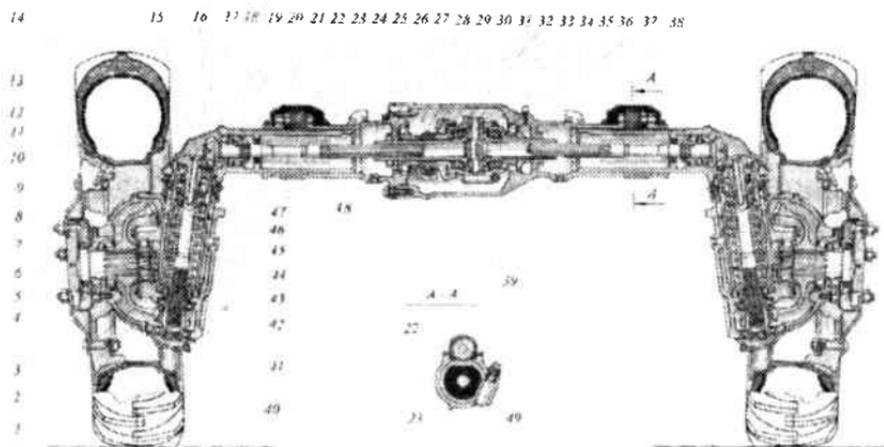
Передний ведущий мост трактора МТЗ - 82: 1, 17, 21, 23 и 36 – крышки; 2, 41 – ведомая и ведущая конические шестерни; 3 – грязевик; 4, 8, 16, 26, 40, 42 – подшипники; 5 – корпус уплотнения; 6, 10, 15, 19, 27, 31– регулировочные кольца и прокладки; 7 – ведомый вал конечной передачи с фланцем для крепления колеса; 9 – стакан подшипника; 11 – диск колеса; 12 – корпус конечной передачи; 13 – стакан с уплотнением; 14 – ведущее колесо; 18 – полуоси; 20 – выдвигной корпус; 22 – червяк; 24 – полуосевые шестерни; 25 – обойма; 28 – корпус дифференциала; 29 – круглая гайка; 30 и 39 – ведомая и ведущая конические шестерни; 32, 37 – фрикционные диски; 33 – нажимная чашка; 34 – оси сателлитов; 35 – сателлит; 36 – крышка; 38 – корпус моста; 43 – пружина; 44 – шворневая труба; 45 – гильза; 46 – вертикальный вал; 47 – упорная шайба; 48 – упорный фланец; 49 – клиновый болт
